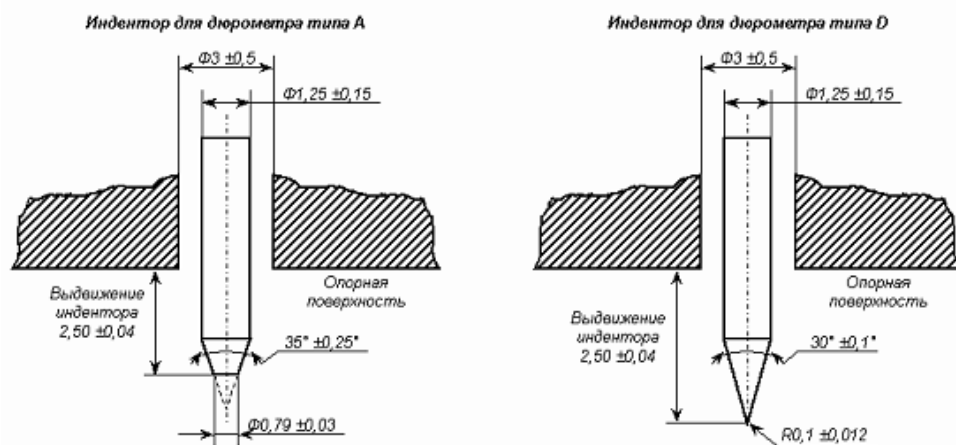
Чертежи инденторов для дюрометров типов А и D
